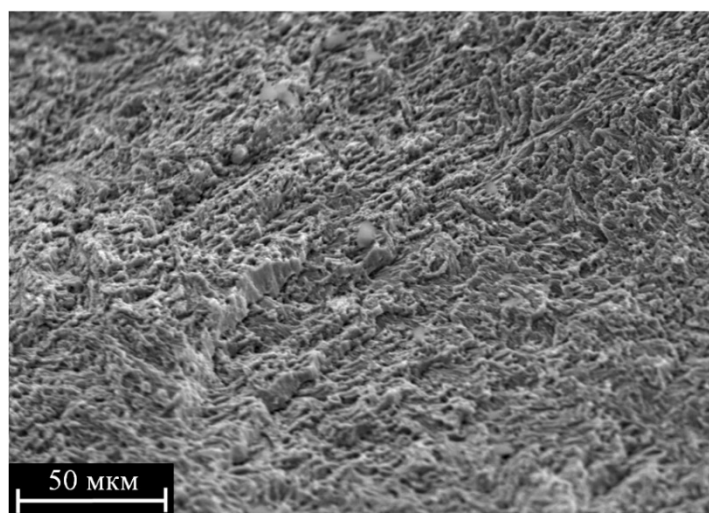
Вязкий характер разрушения в зоне сварного шва с 25 % Nb
